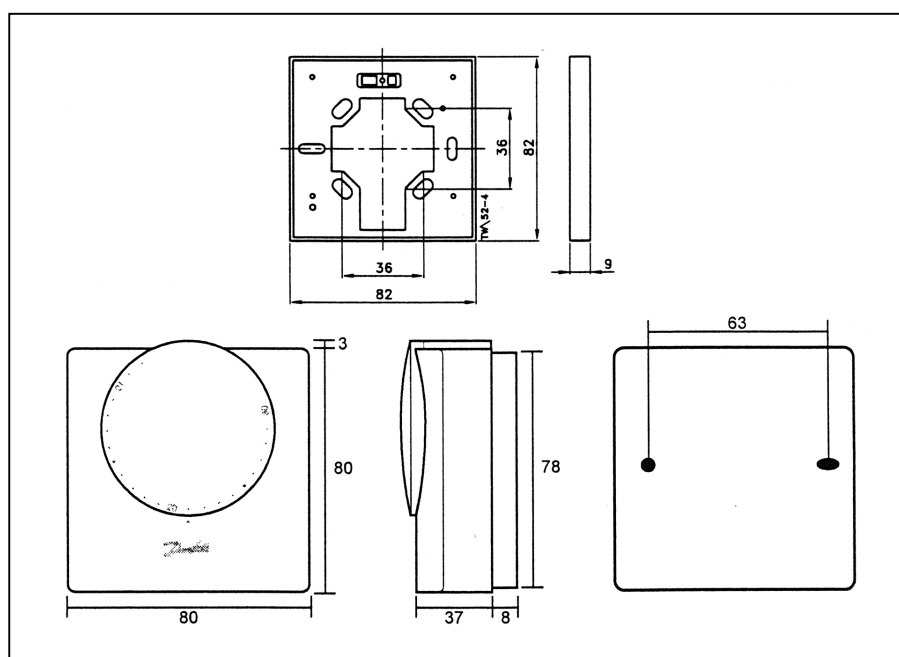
Габаритные и присоединительные размеры термостата RMT.
